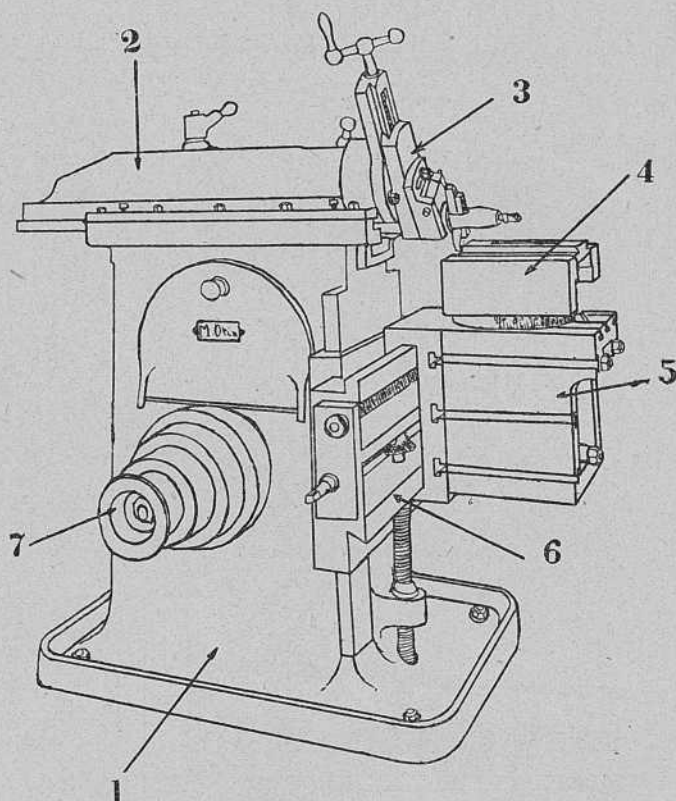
Limadora. 1, bancada; 2, carro porta-herramienta; 3, charriot; 4, tornillo; 5, mesa; 6, carro vertical; 7, cono-polea.
